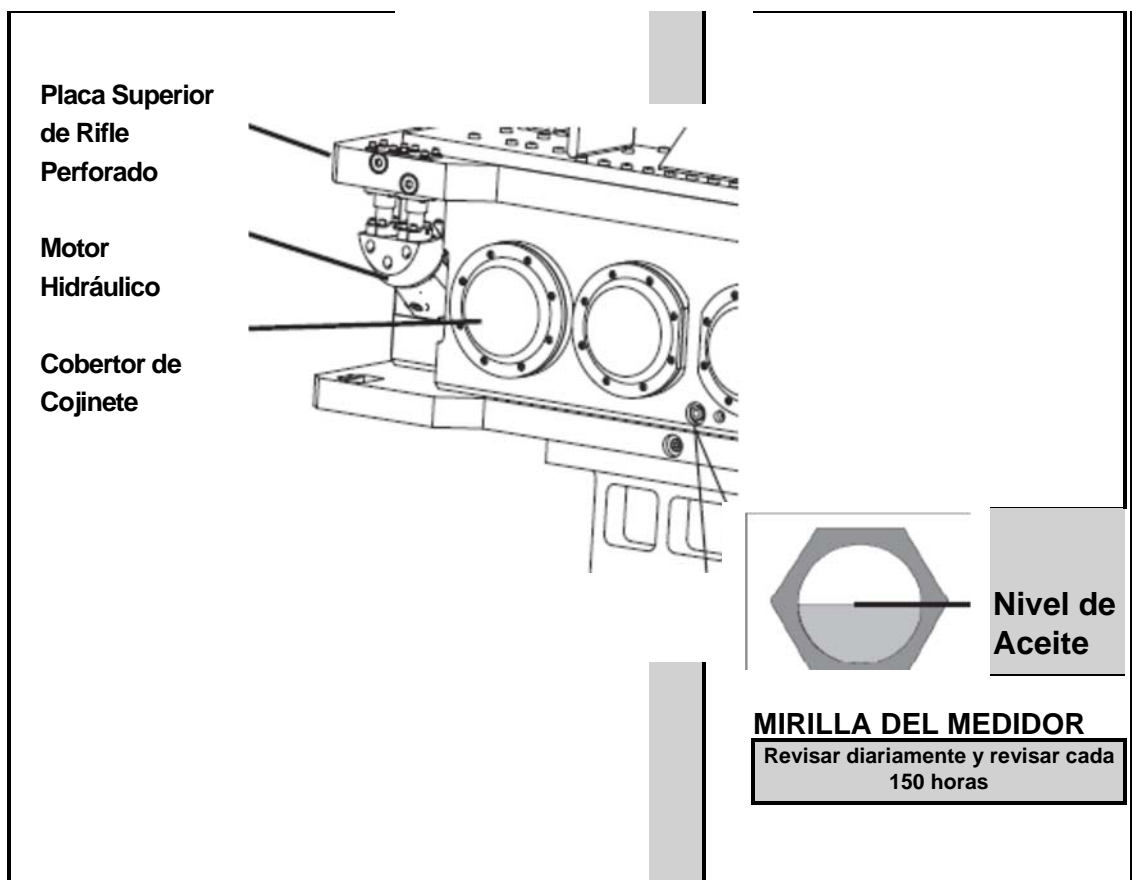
D. Descripción General de Caja de Engranaje Vibratoria.
